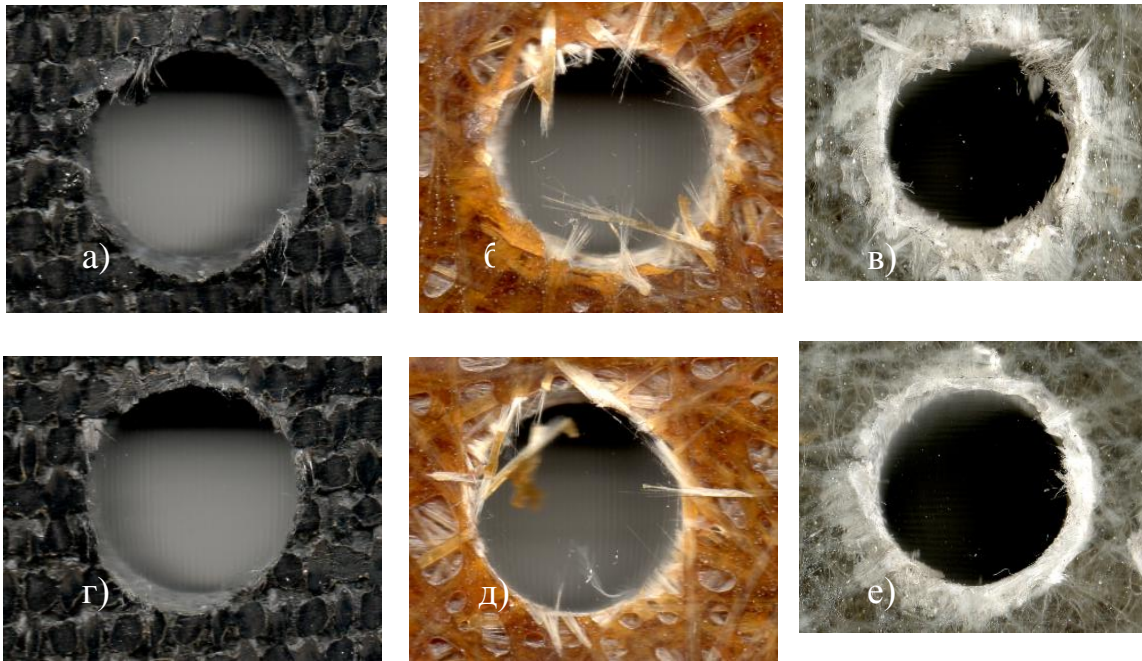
Поверхности выхода резьбообрабатывающего инструмента:
